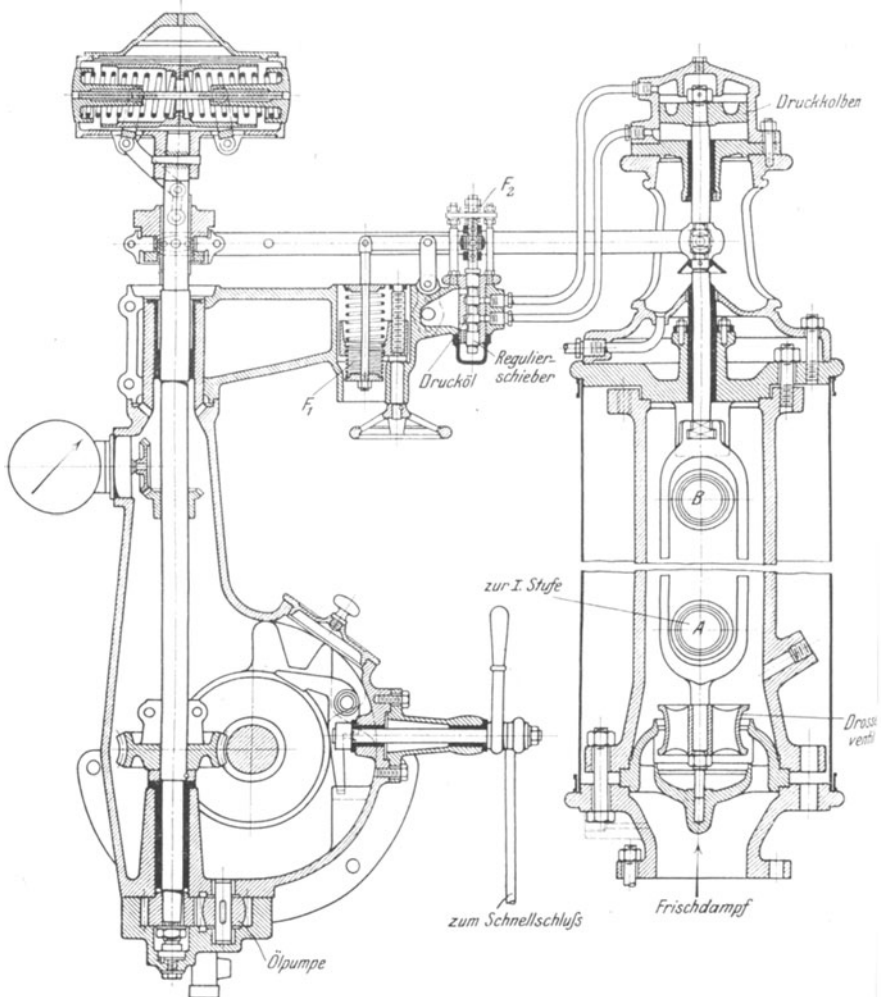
Regulator mit Druckölsteuerung für den Dampfeinlaß in die Turbine.
